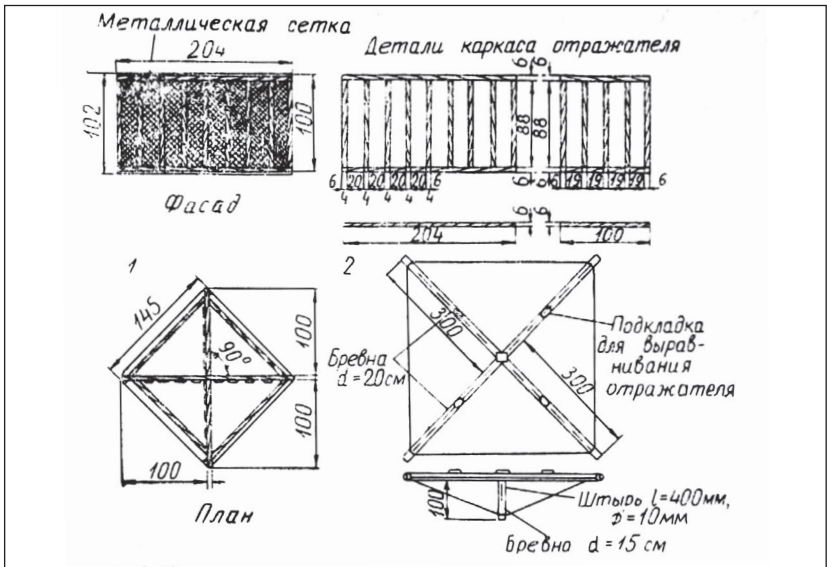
Уголкового отражатель К4-100 войскового изготовления:
